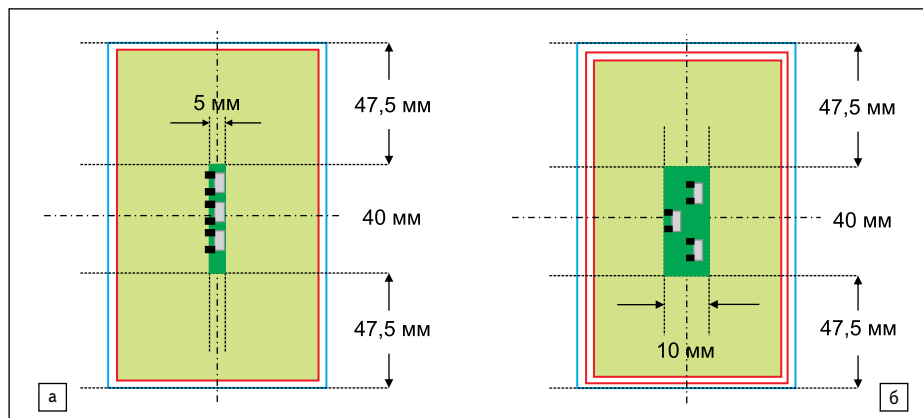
Корпус EHz: а) с однослойной экранировкой; б) с двухслойной экранировкой
